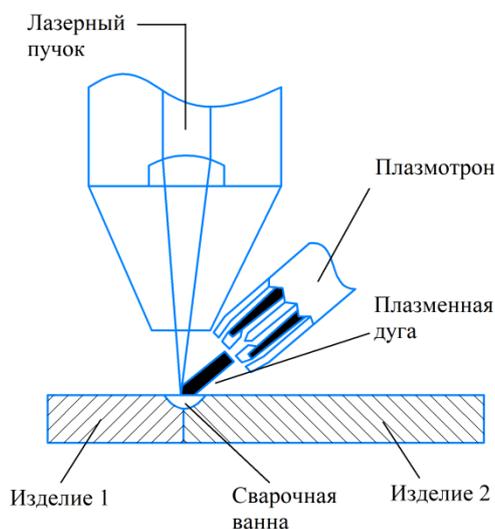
Схема процесса последовательной лазерно-плазменной сварки
